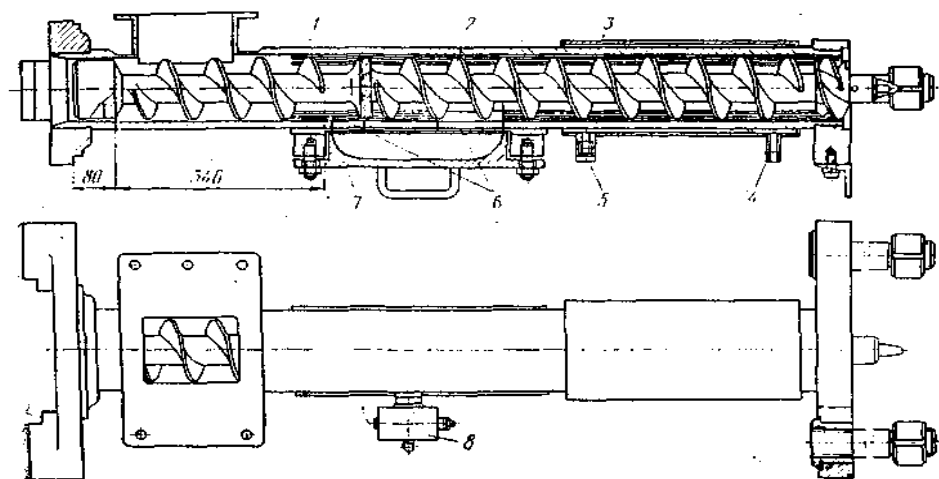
Пристрій преса ЛПЛ-2М
